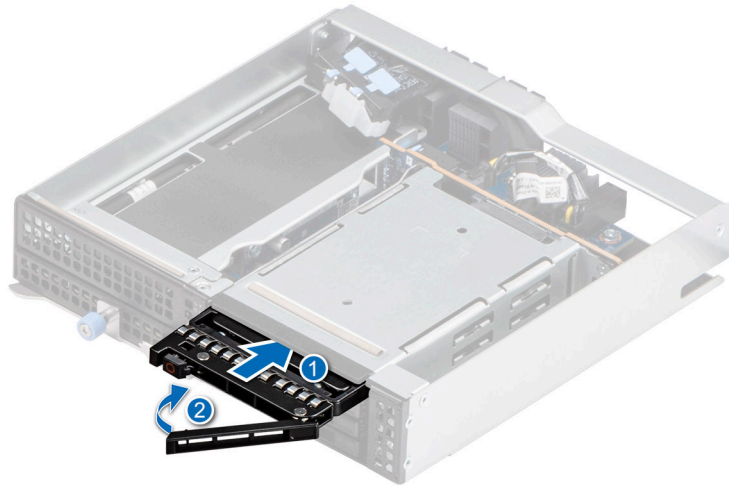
Installation d'un support de disque de 2,5 pouces dans le module d'extension
